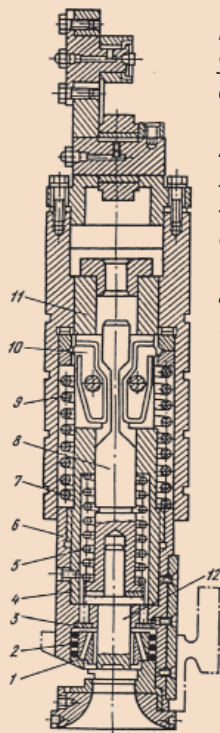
Закупорювальний ударно-обтискний механізм для кронен-пробок:
